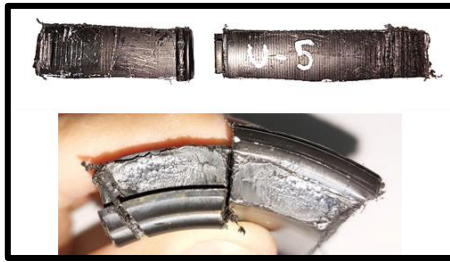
Unión del flange adapter – codo de 90° sufre fractura frágil justo en la unión.
